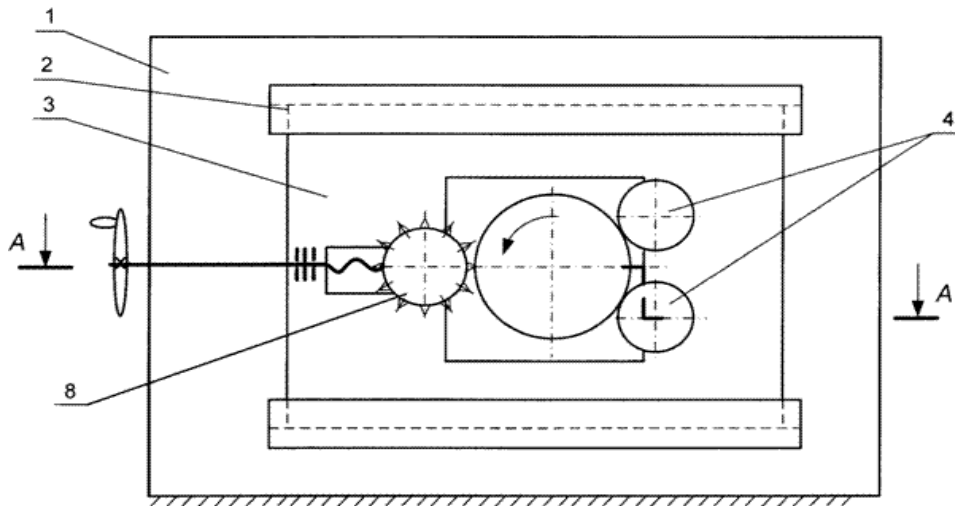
Схема устройства для обработки заготовок из пластмасс, при точении их на токарном станке
